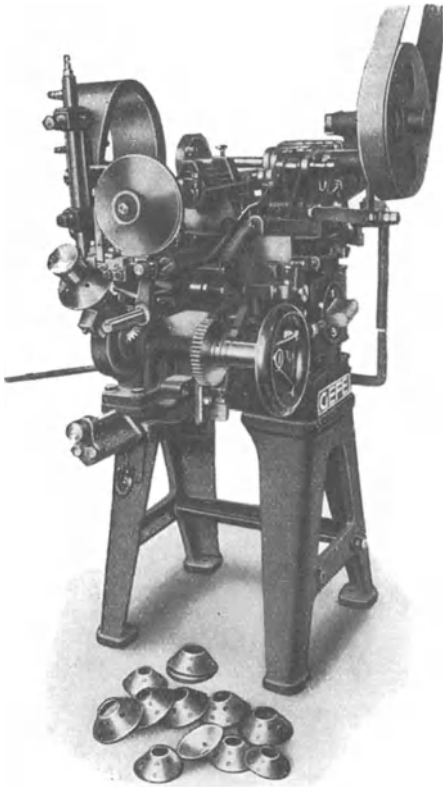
Sonder-Punktschweißmaschine für Blechtrichter.
